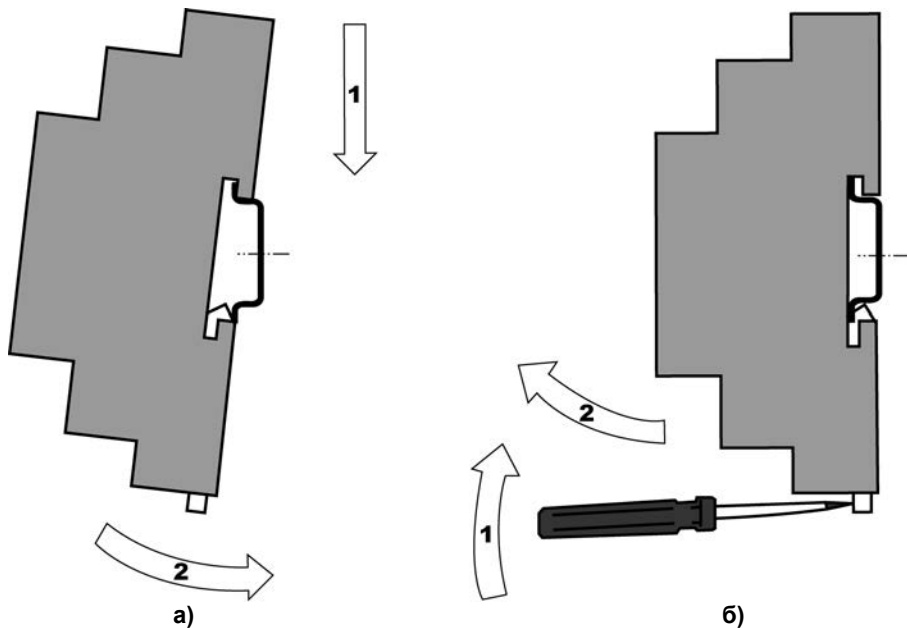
Монтаж контроллера с креплением на DIN-рейку
